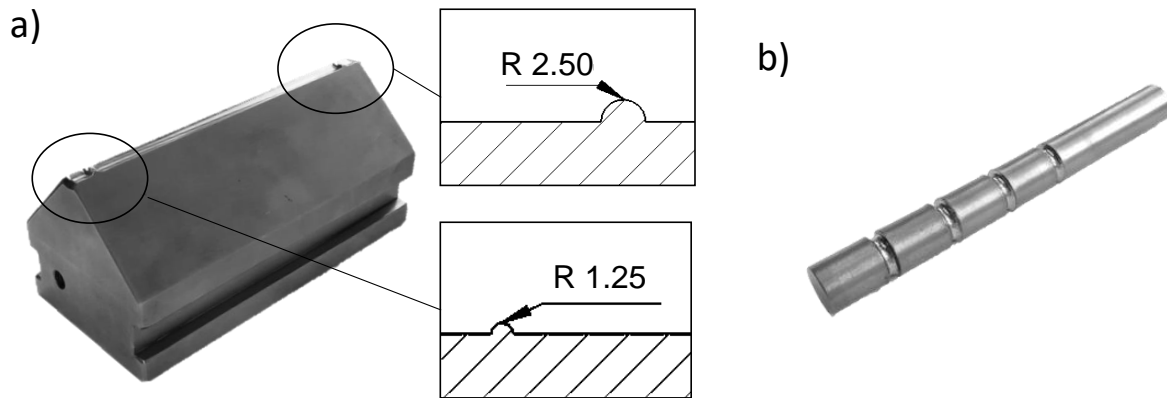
Werkzeug zum Rundkneten (a) und Stab mit eingebrachten Kerben (b).
